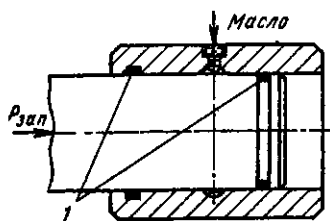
Схема сборки цилиндрического соединения путем нагнетания масла: 1 – уплотнительные кольца
